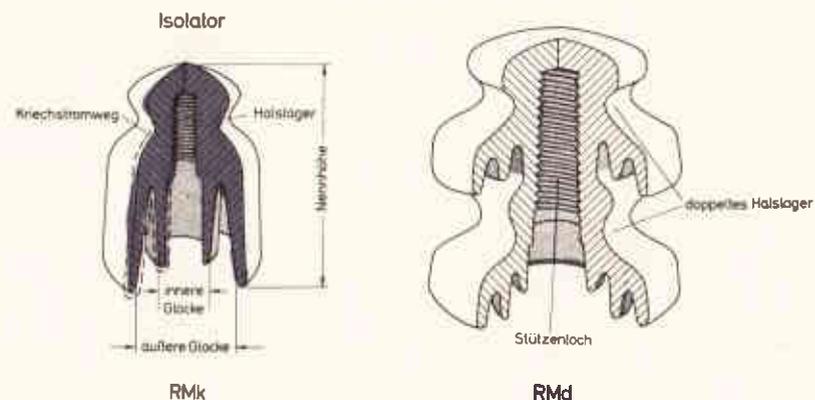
Isolatoren für Blankdrahtleitungen
